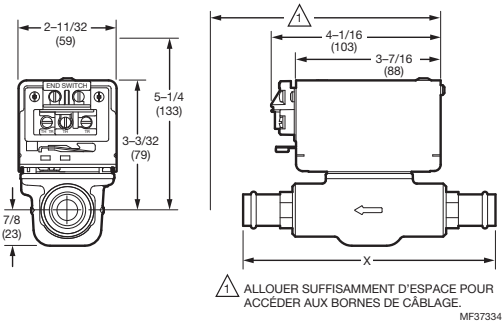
Dimensions (V8043F). Mesures en po (mm). Voir le Table 1.
